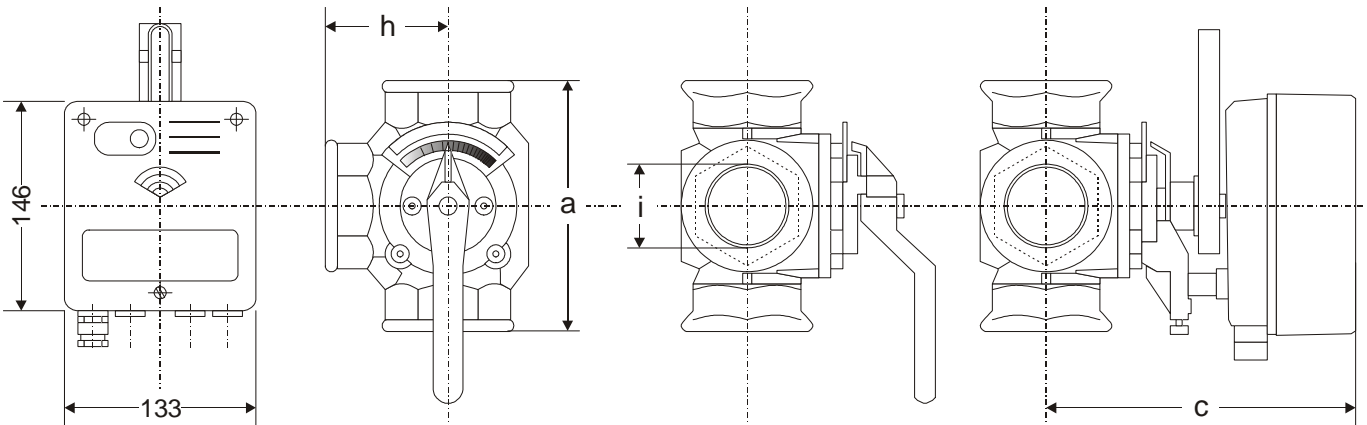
VMM et DRxxxGMLA, dimensions (en mm)
